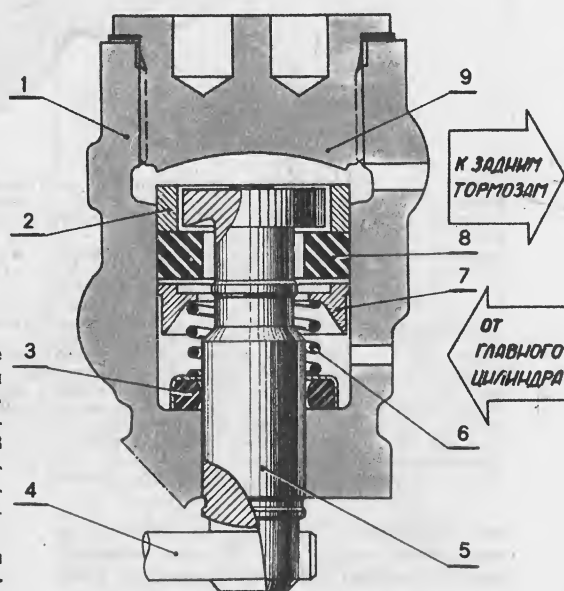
Устройство регулятора тормозного усилия задних колес: 1 — корпус; 2 — кольцо; 3, 8 — уплотнитель; 4 — торсион; 5 — поршень; 6 — пружина; 7 — упорное кольцо; 9 — пробка.
